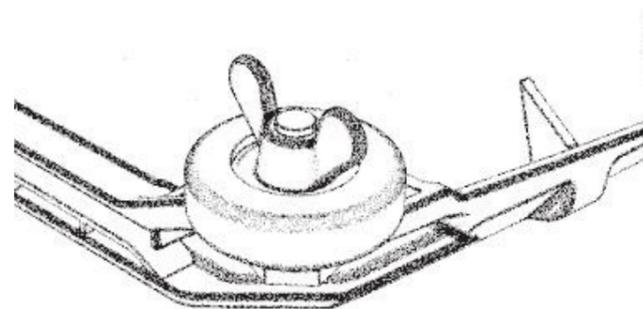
Schéma d'achèvement de l'installation de la poulie droite
